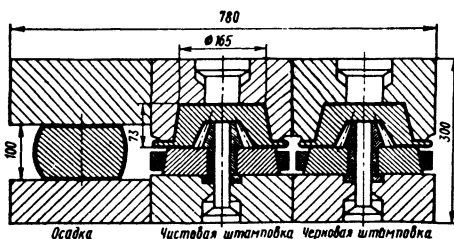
Мастер-штамп для штамповки на КГШП зубчатых вкладышей для изготовления поволоков сателлитов
